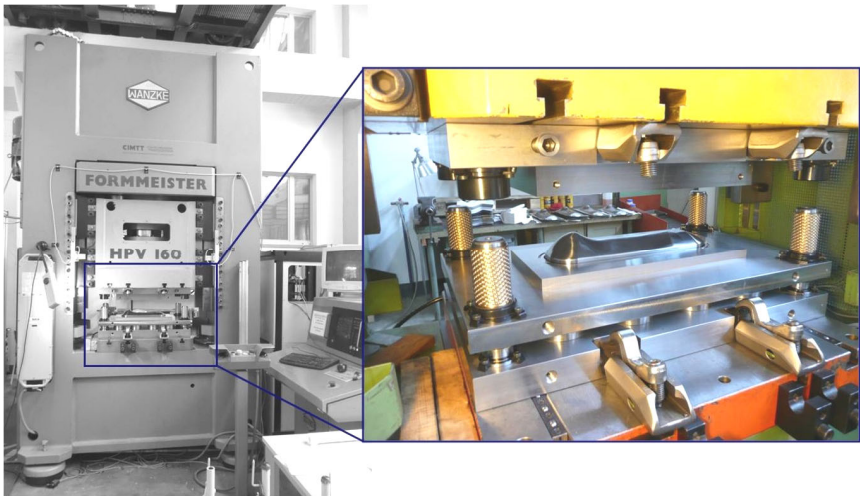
Hydraulische Presse mit eingebautem Tiefziehwerkzeug
